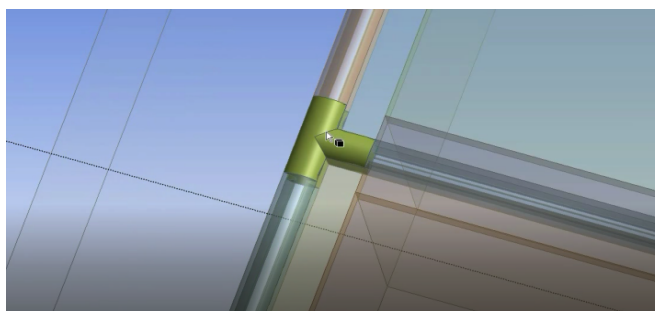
Основні розрізи зварног шва та пластин
